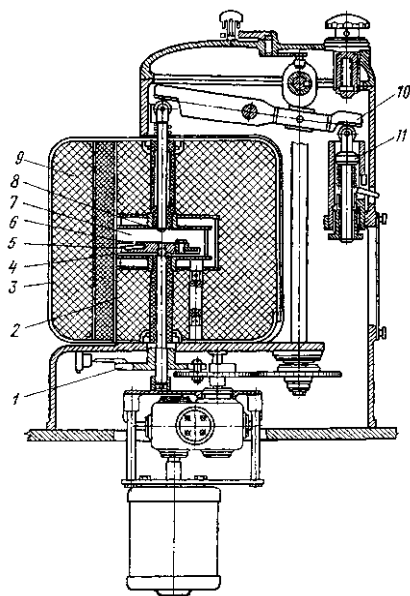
Устройство прибора для определения температуры хрупкости пластмасс: 1 – привод; 2 – изоляция; 3 – криокамера; 4 – зажим; 5 – образец; 6 – термопара; 7 – испытательная камера; 8 – пуансон; 9 – дверь; 10 – рычаг; 11 – пружинный механизм.
